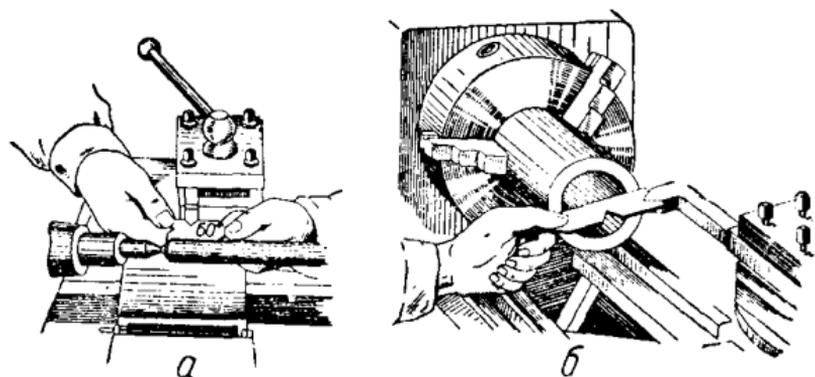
Установка резьбового резца по шаблону при нарезании резьбы:
